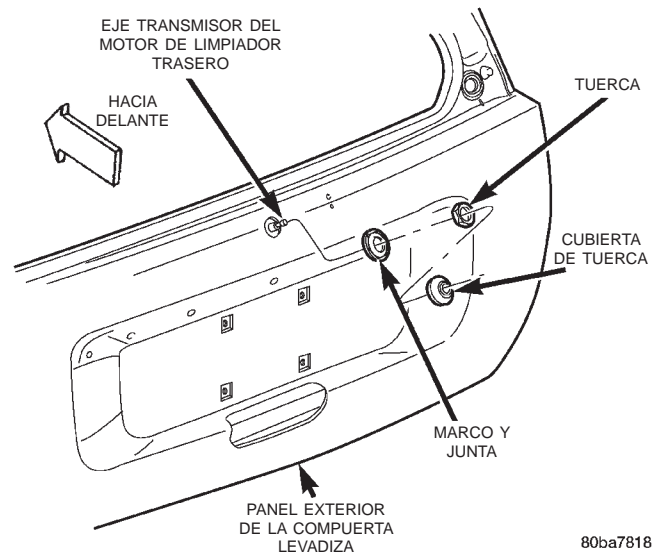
Desmontaje e instalación del eje transmisor del motor de limpiador trasero
